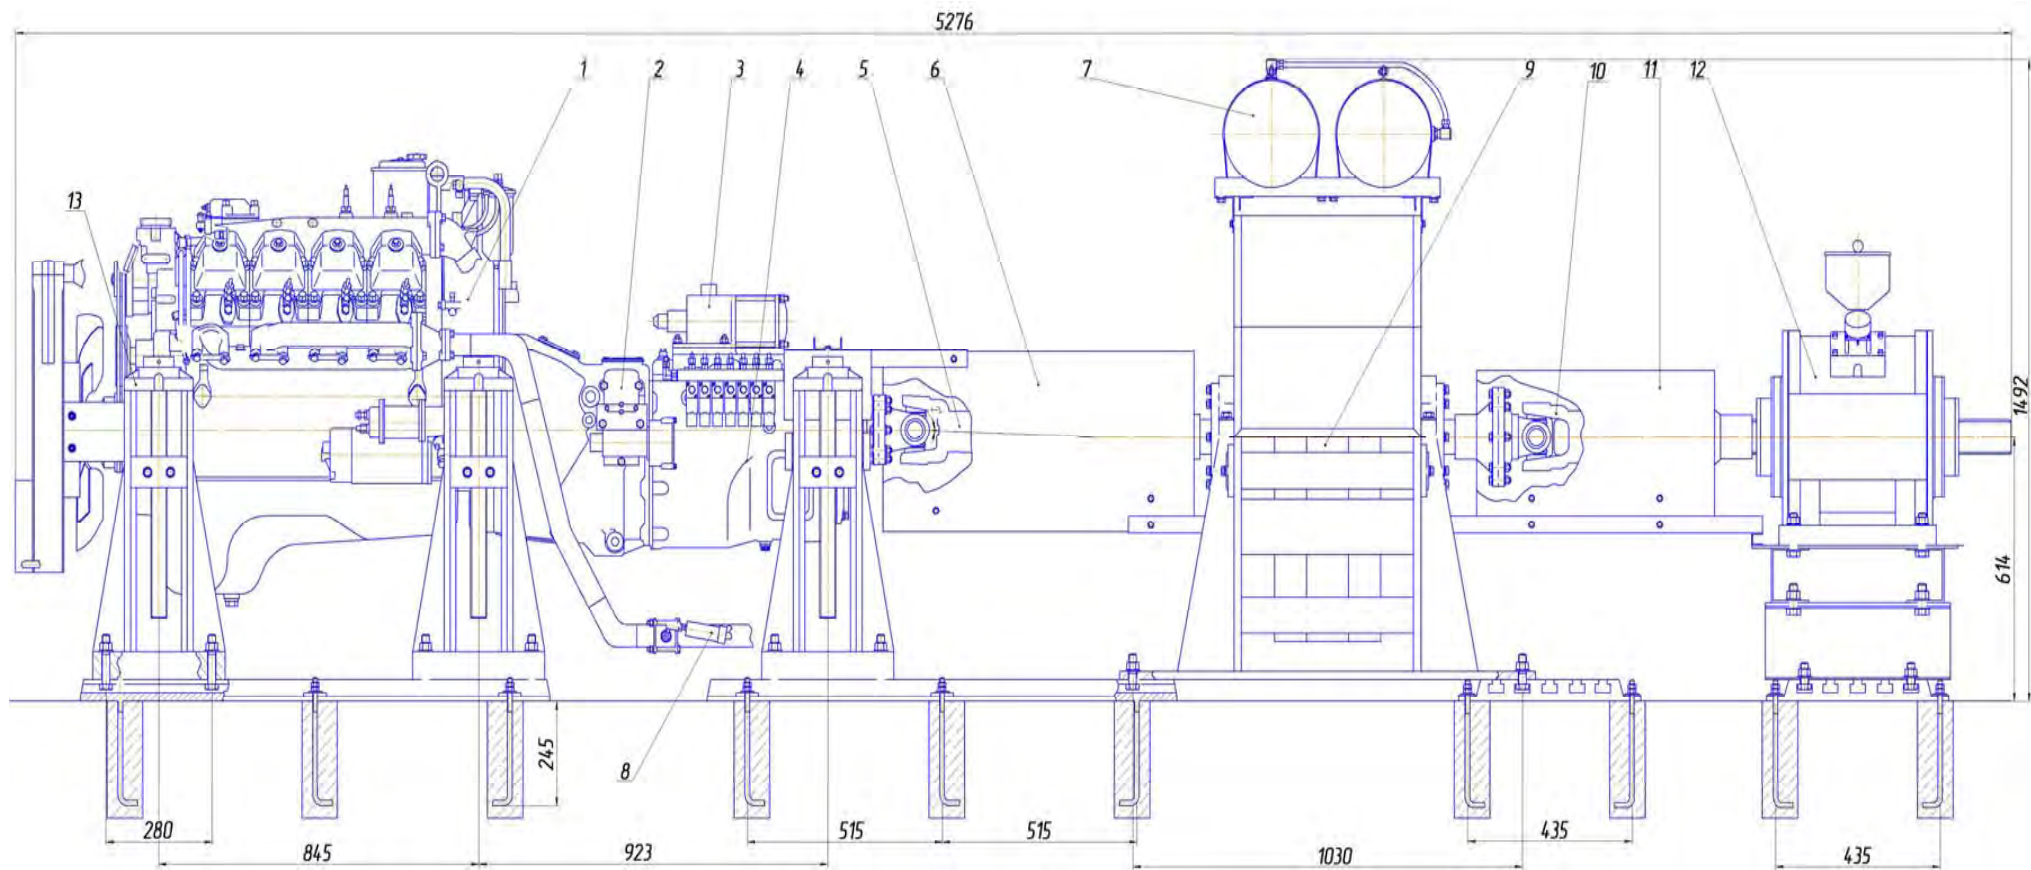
Основные габаритные размеры и компоновка узлов и агрегатов испытательного стенда:
